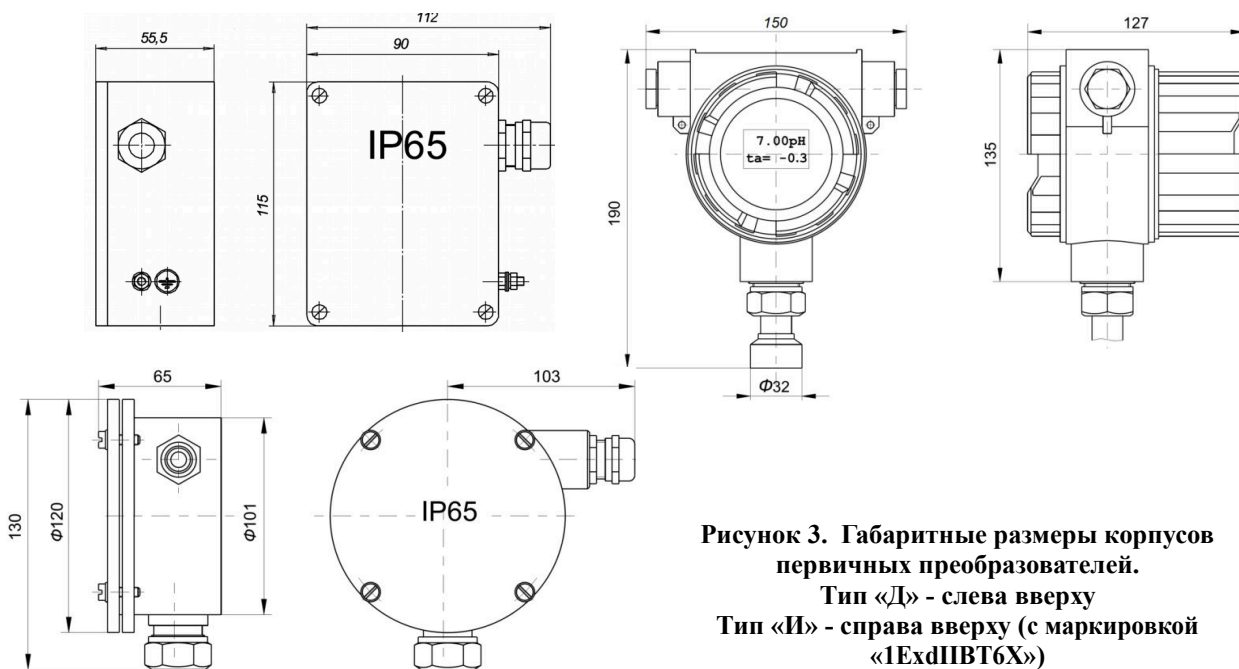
Габаритные размеры корпусов первичных преобразователей.
